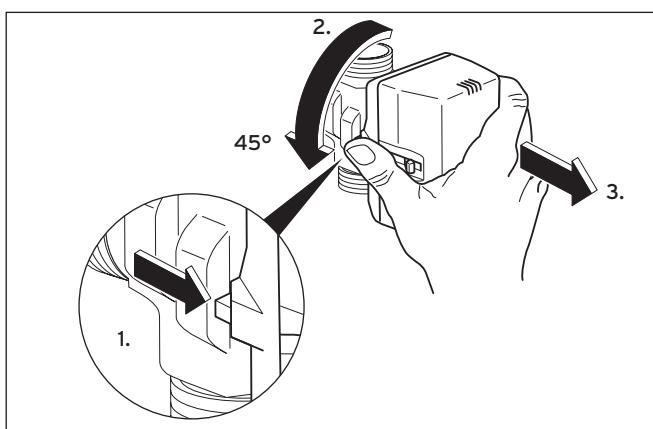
Снятие корпуса двигателя клапана рассольной смеси
